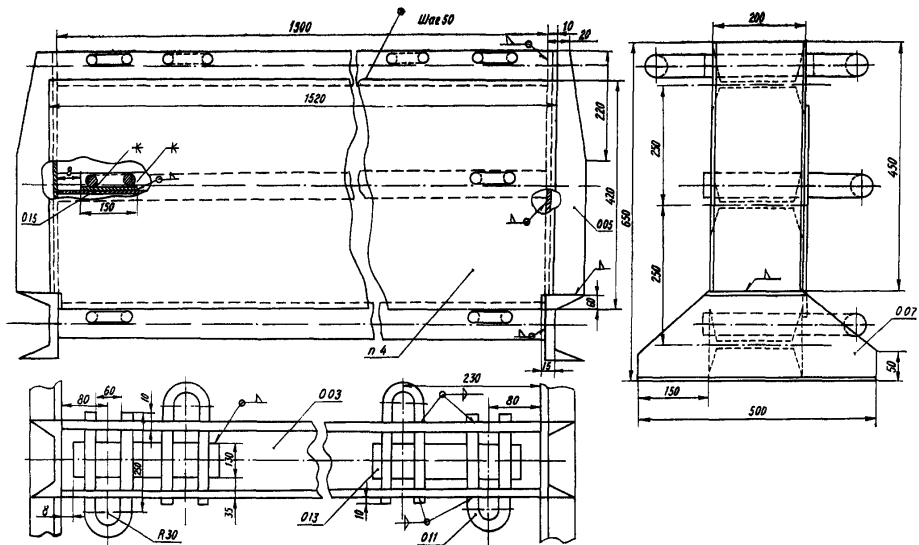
Стенка упорная. Сборочный чертеж Э26-94-420
